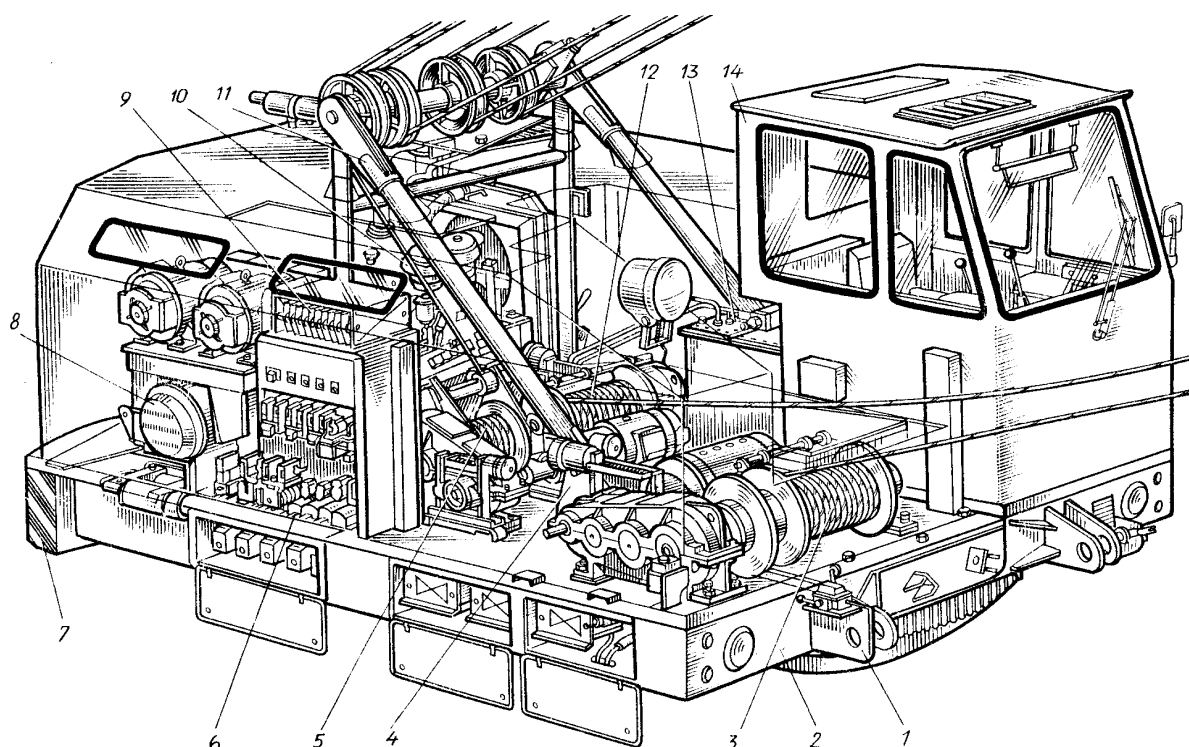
Поворотная платформа крана с канатной подвеской рабочего оборудования
